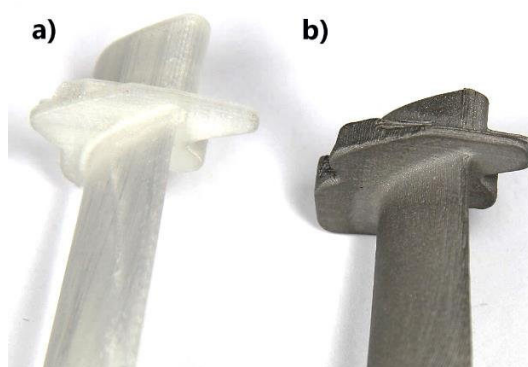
Model produktu určený ke zpracování technologií přesného lití vyrobený metodou Binder Jetting.
